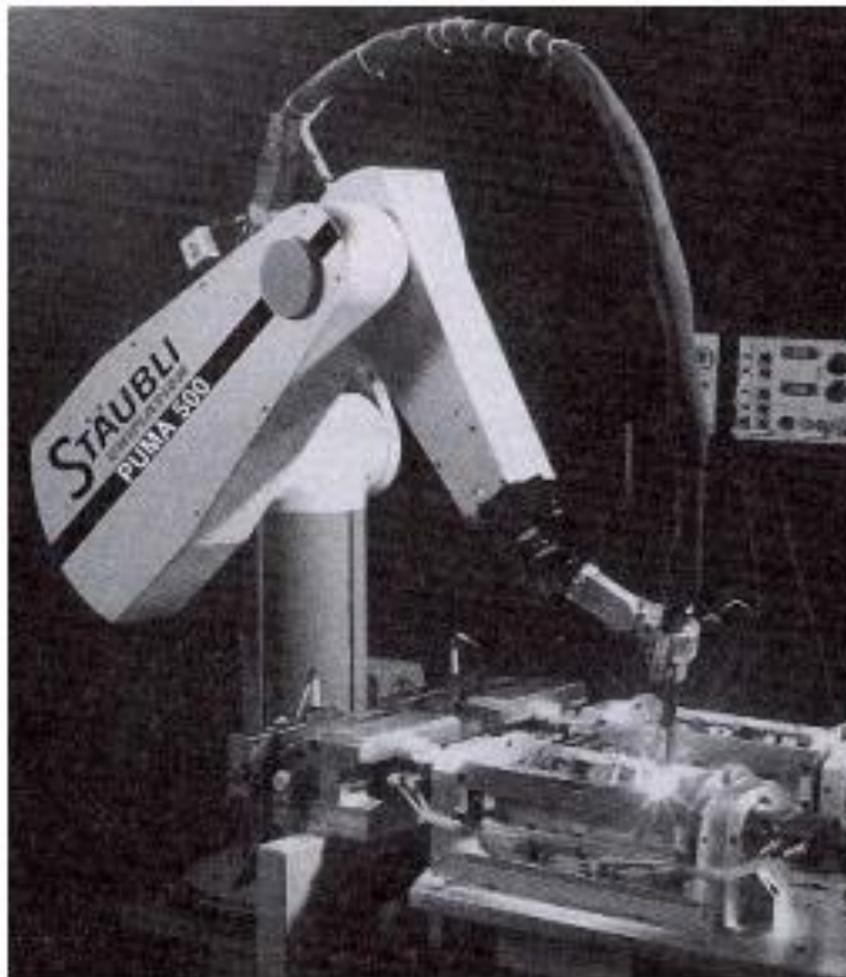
Foto do robô Puma. (Fonte: Pires 2002)
